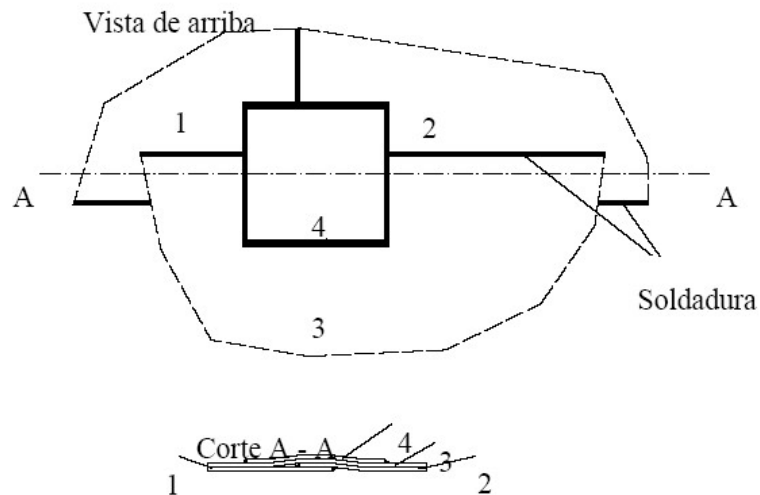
Soldadura tipo T con parche a la unión de tres capas
